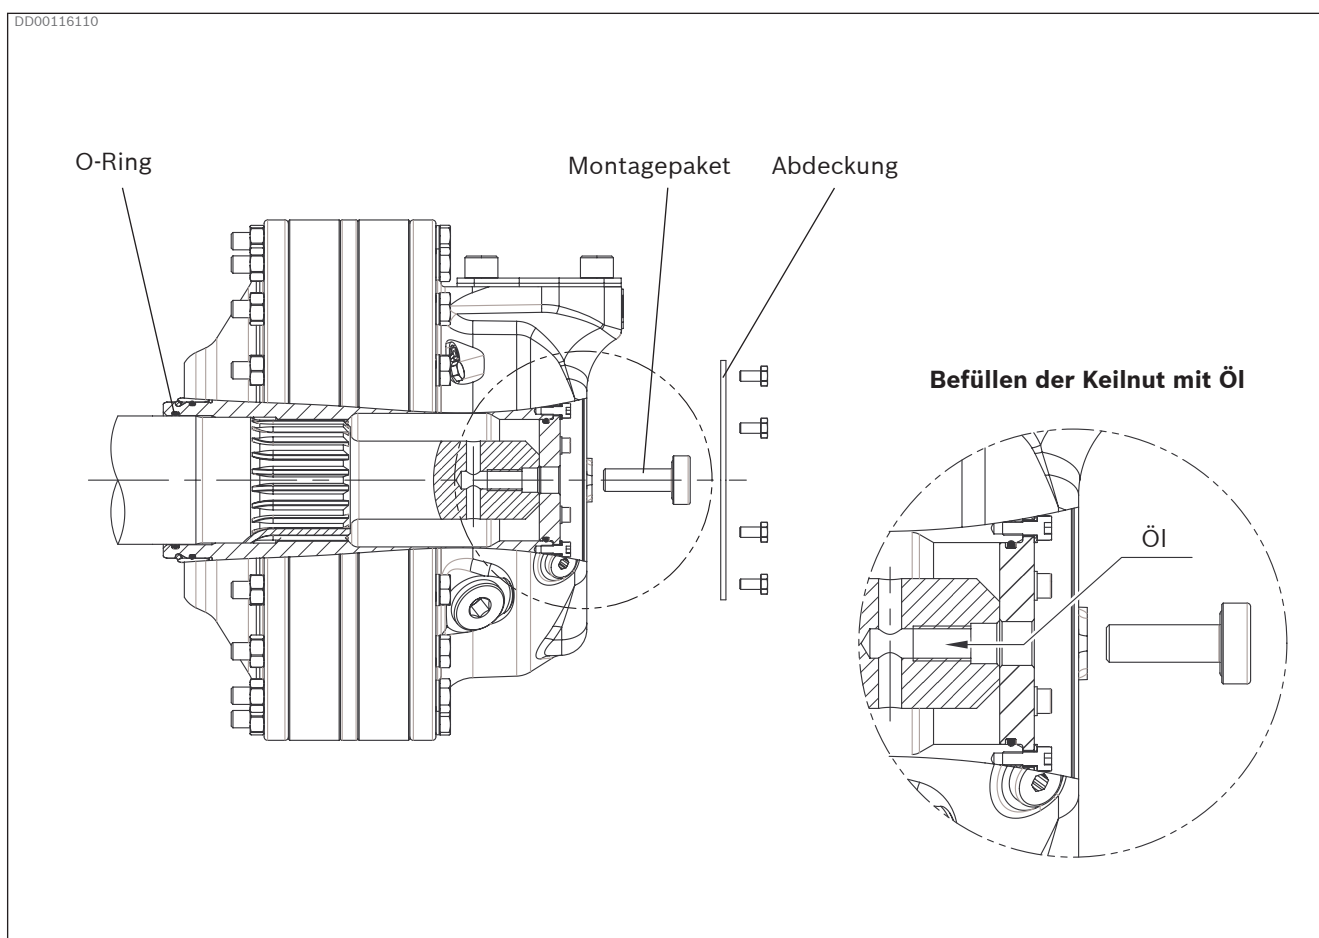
Befestigen Sie den Motor mit Keilnut mithilfe des Montagepaketes, waagerechte Montage.
